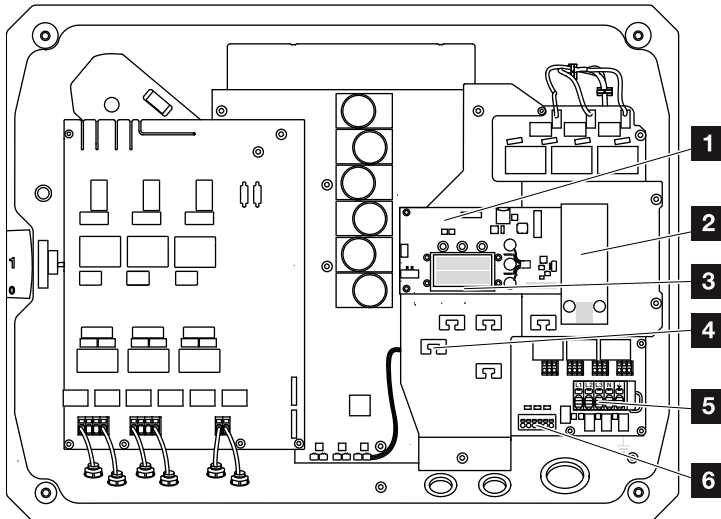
PIKO-Wechselrichter 15 - 20 (Innenansicht)
